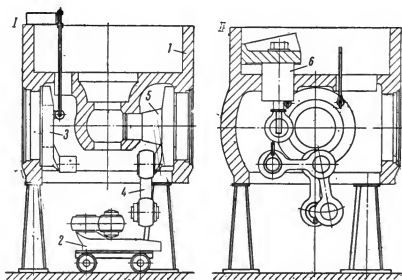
Сборка механизмов поворота бескостяшного рабочего колеса.
